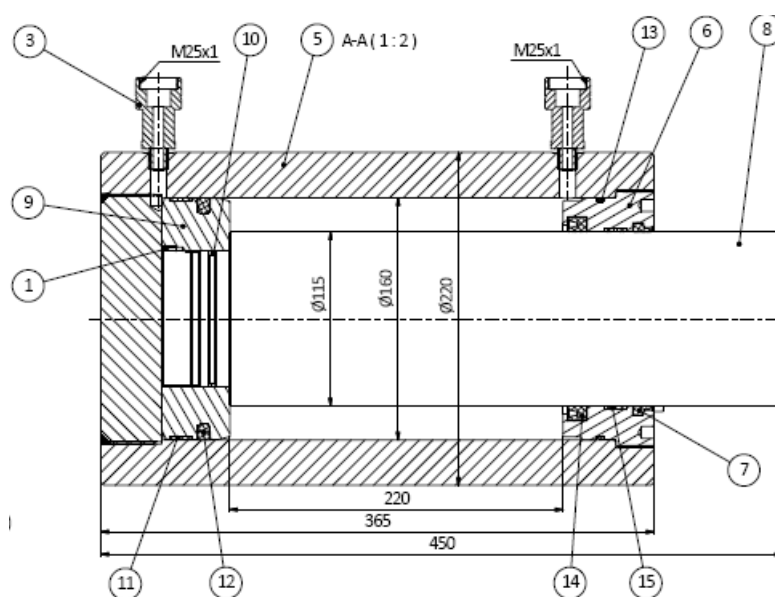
Cilindru hidraulic vertical DA 140 T
